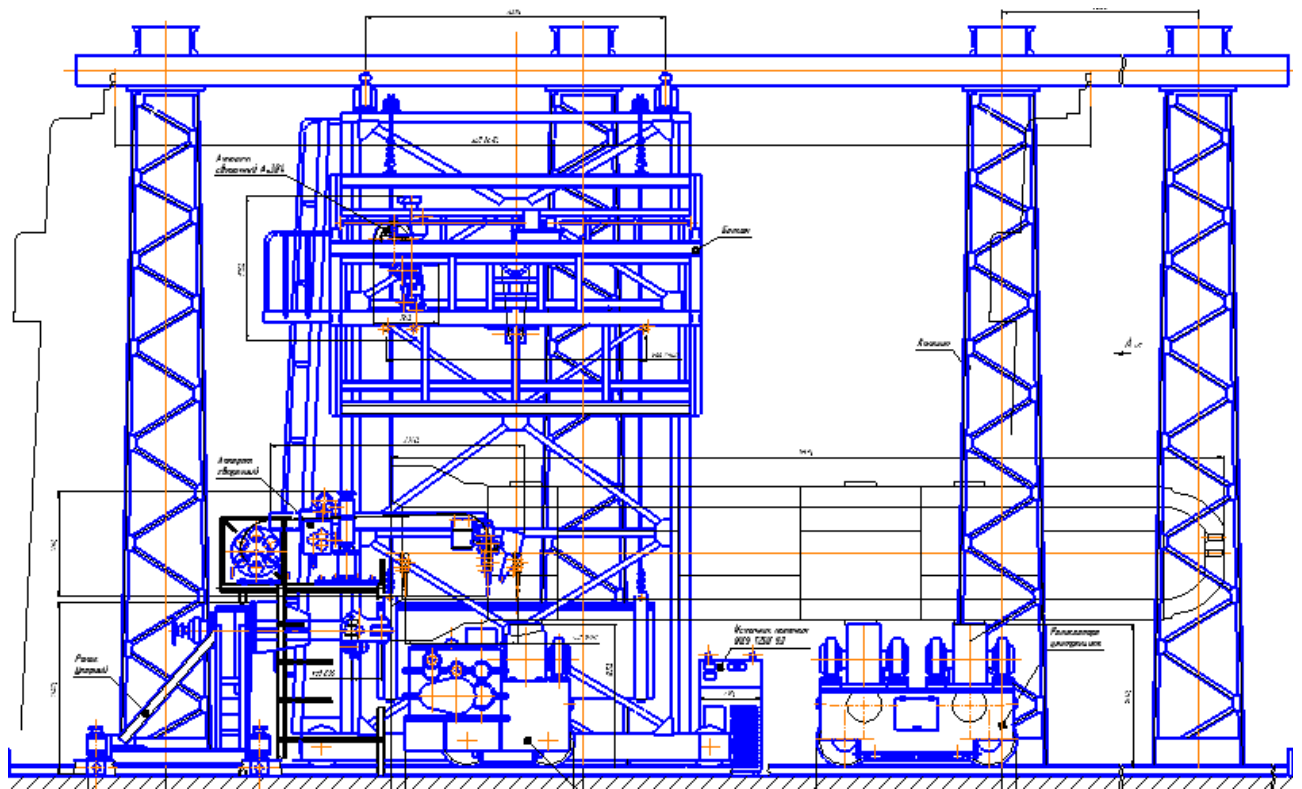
Загальний вигляд стану для виготовлення корпусу реактору [6]
